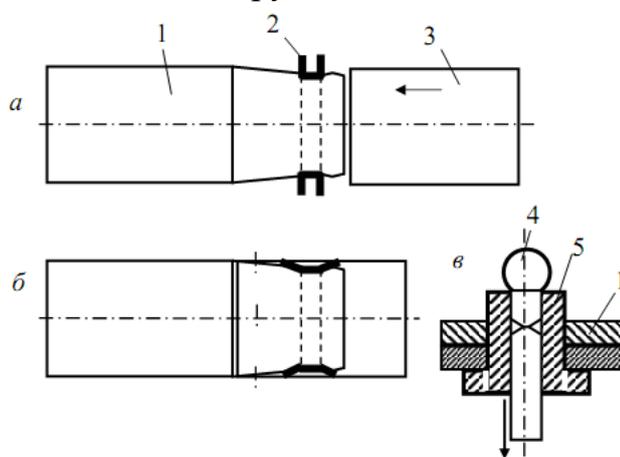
Способ соединения труб по длине: а – подготовка труб для сборки; б – труба после сборки; в – способ установки заклепок
